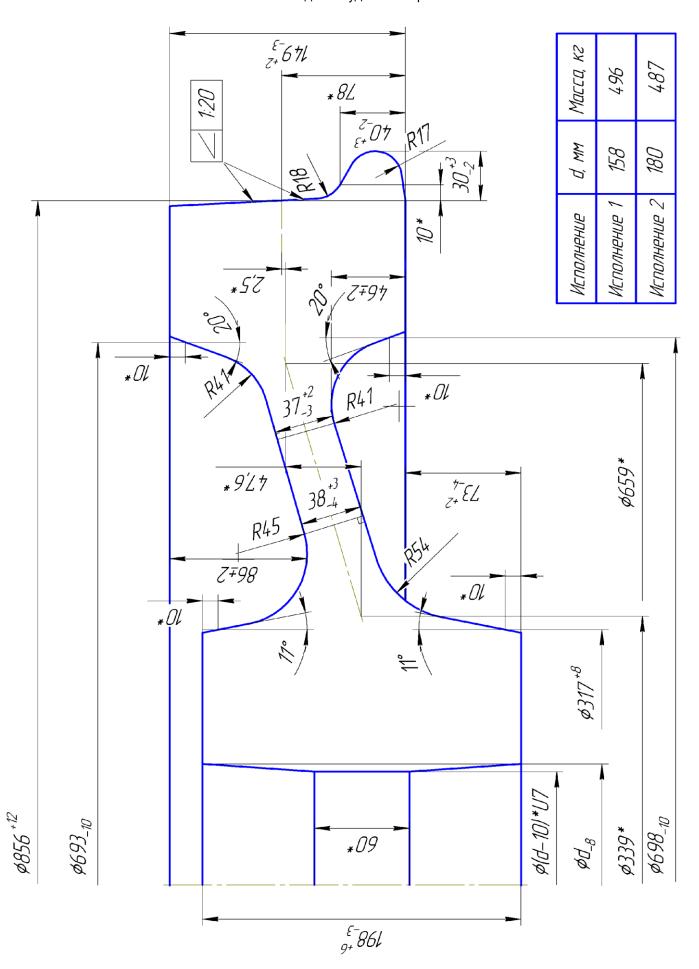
Колесо без механической обработки Ø 856 мм (под чистовое Ø 838,2 черт. № KP-0064-15).
